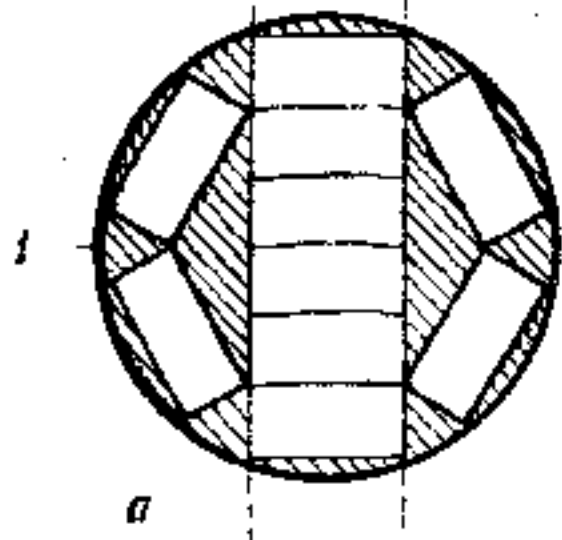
Расположение дрок в пакете заготовки винта.
